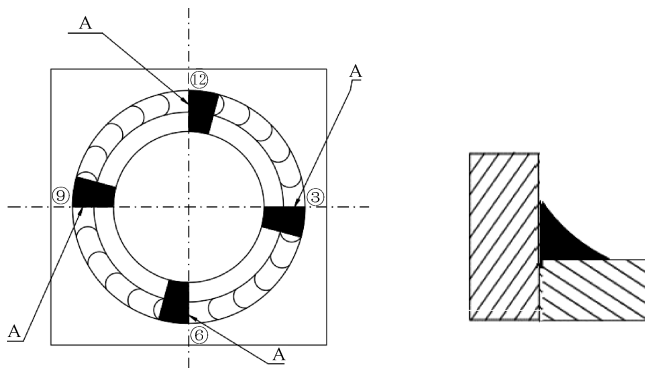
管板角焊缝宏观金相取样位置
